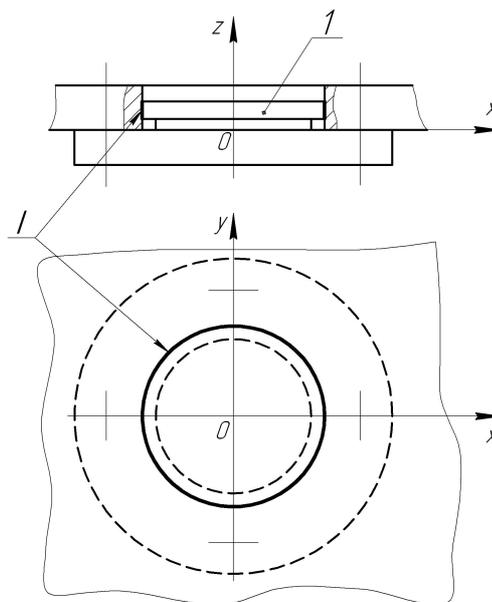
Схема базирования с двойной опорной базой: I – двойная опорная база детали; 1 – деталь
